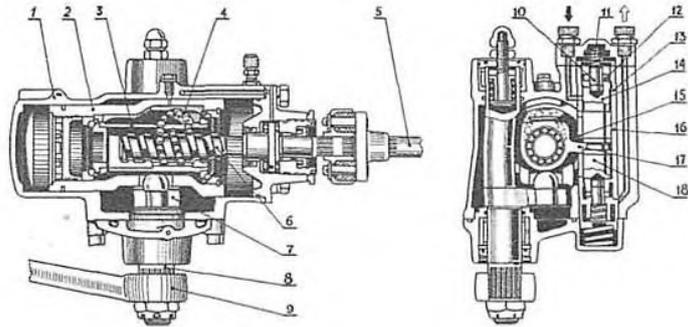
Элементы сервомеханизма рулевого управления автомобиля «Даймлер-Бенц-300»: 1 — картер рулевой передачи; 2 — рабочий поршень; 3 — гайка рулевой передачи; 4 — винт с шаровой гайкой; 5 — рулевой вал; 6 — червяк рулевой передачи; 7 — рычаг поворотной цапфы; 8 — вал сошки ру-
